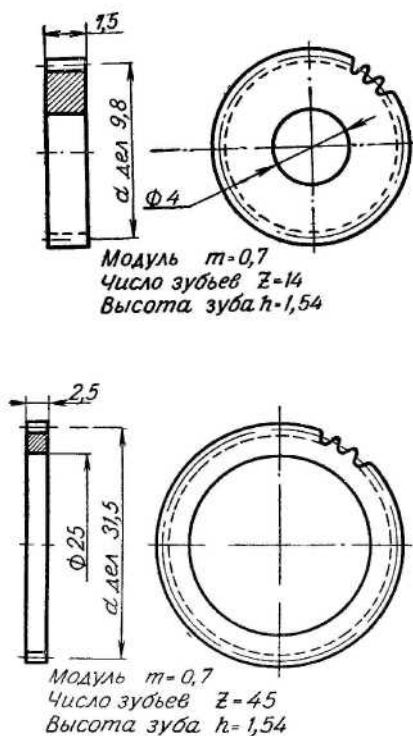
Шестерня 3 (вверху); шестерня 8 (снизу)
